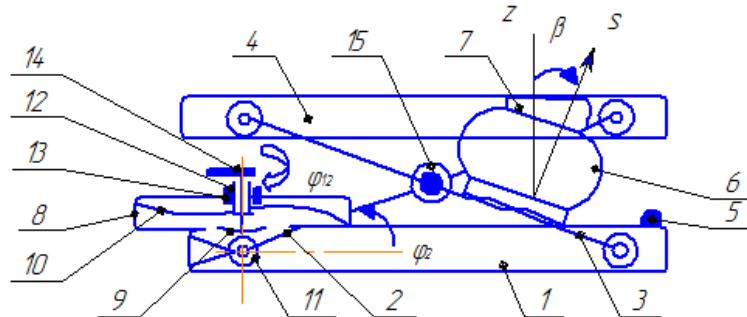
Патент № 2438888: 1 – основание; 2 – входное звено; 3 – промежуточные звенья (рычаги); 4 – звено; 5 – ограничители хода; 6 – замкнутая резинокордная оболочка; 7 – опорные обтекатели; 8 – корпус; 9,11 – колеса конической передачи; 10 – набор пластинчатых пружин; 12 – втулка; 13 – подшипниковая опора; 14 – рычаг; 15 – датчик угловых перемещений
